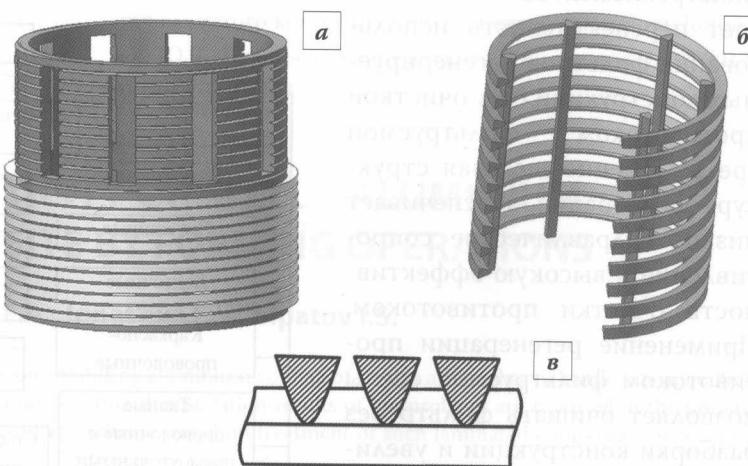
Каркасно-проводочные сварные фильтры: а – корпусного типа; б – на основе стрингеров; в – вариант треугольной формы сечения проволоки
